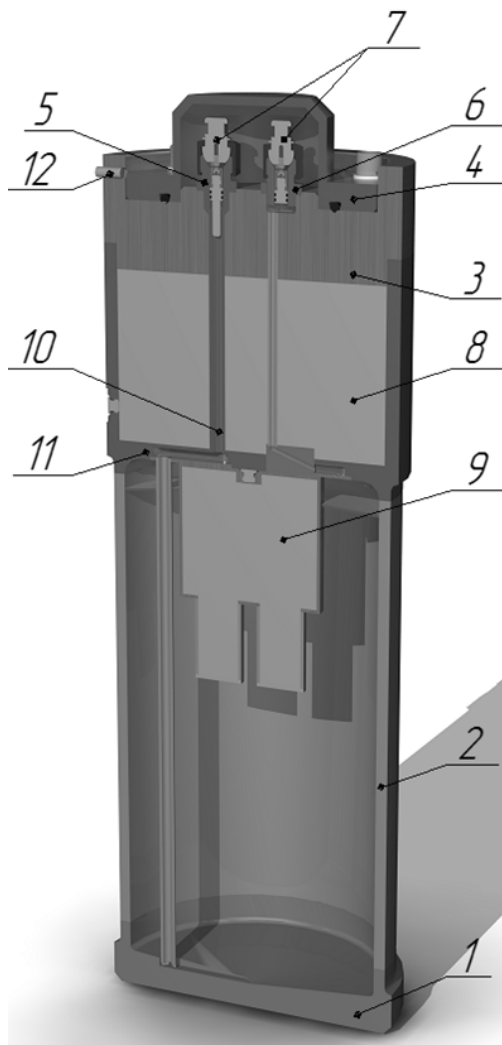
Пенал: 1 – дно; 2 – обечайка; 3 – колпак; 4 – защитная крышка; 5 – штуцер топливный; 6 – штуцер газовый; 7 – пробка; 8 – защита; 9 – защита; 10 – канал; 11 – переборка; 12 – штифт
